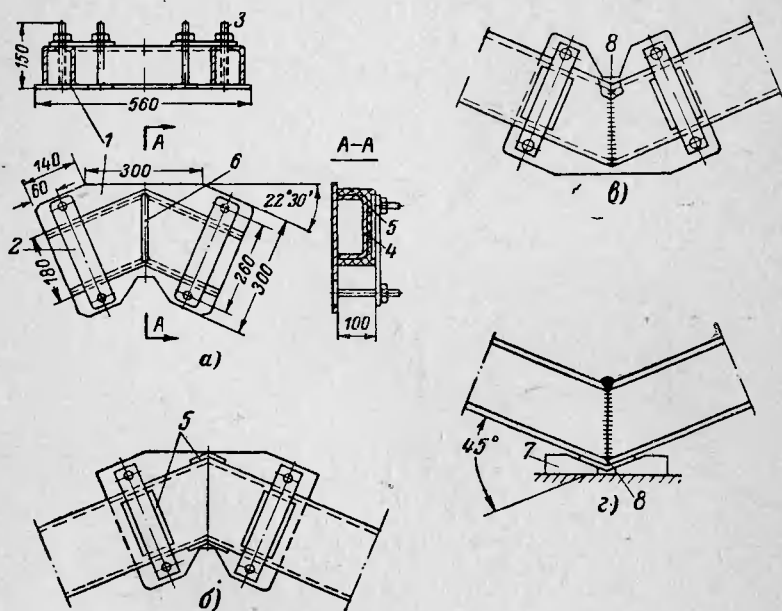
Сварка двух шин размером $200 \times 90 \times 10$ мм под углом 45° .
